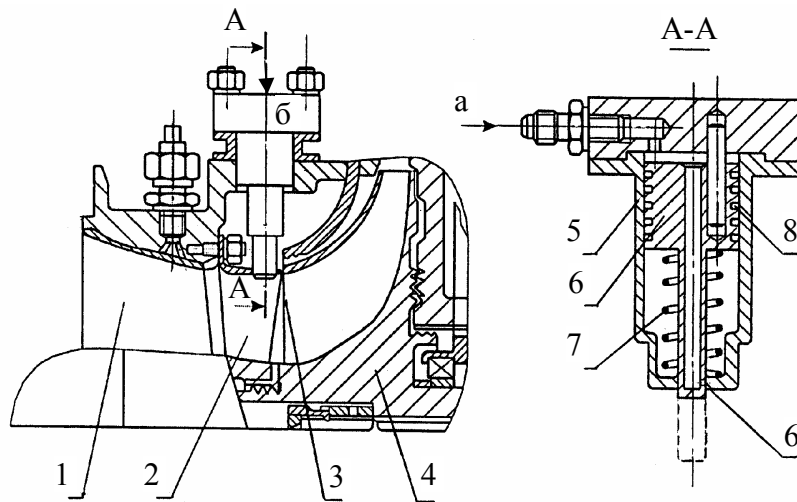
Агрегат пилоочищення компресора низького тиску:
